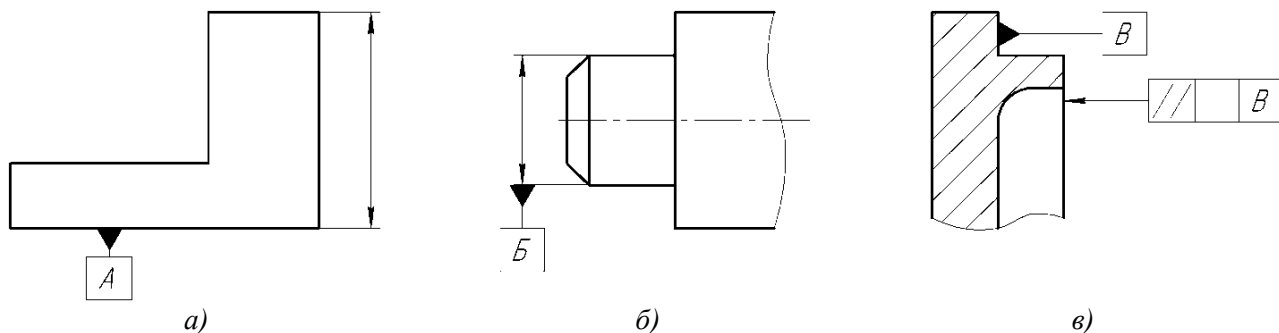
Правила нанесения условных обозначений баз на чертежах деталей
